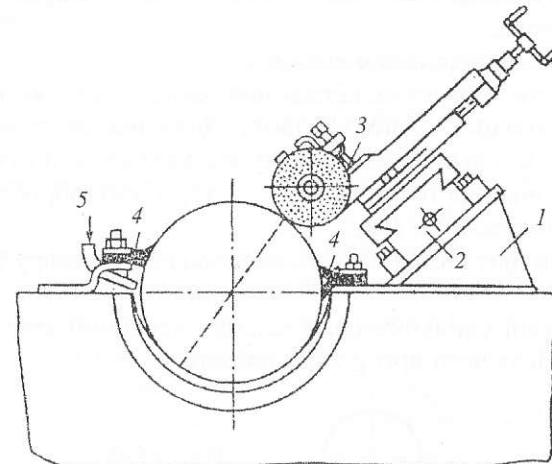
Пристрій для ремонту опорних шийок вала у власних підшипниках:
